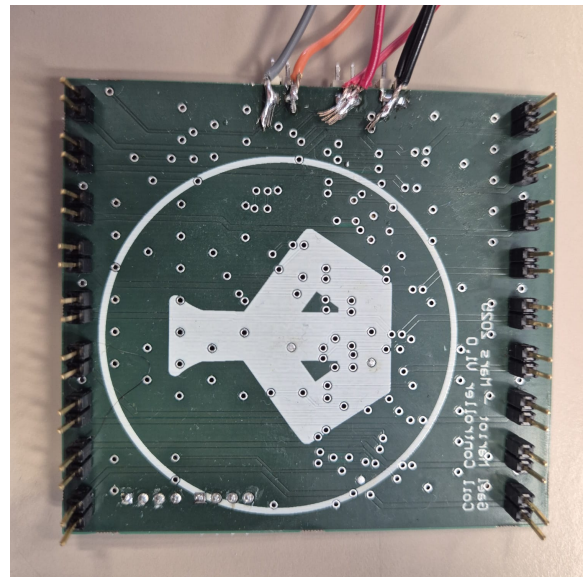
Verso de la carte de contrôle complète et assemblée
